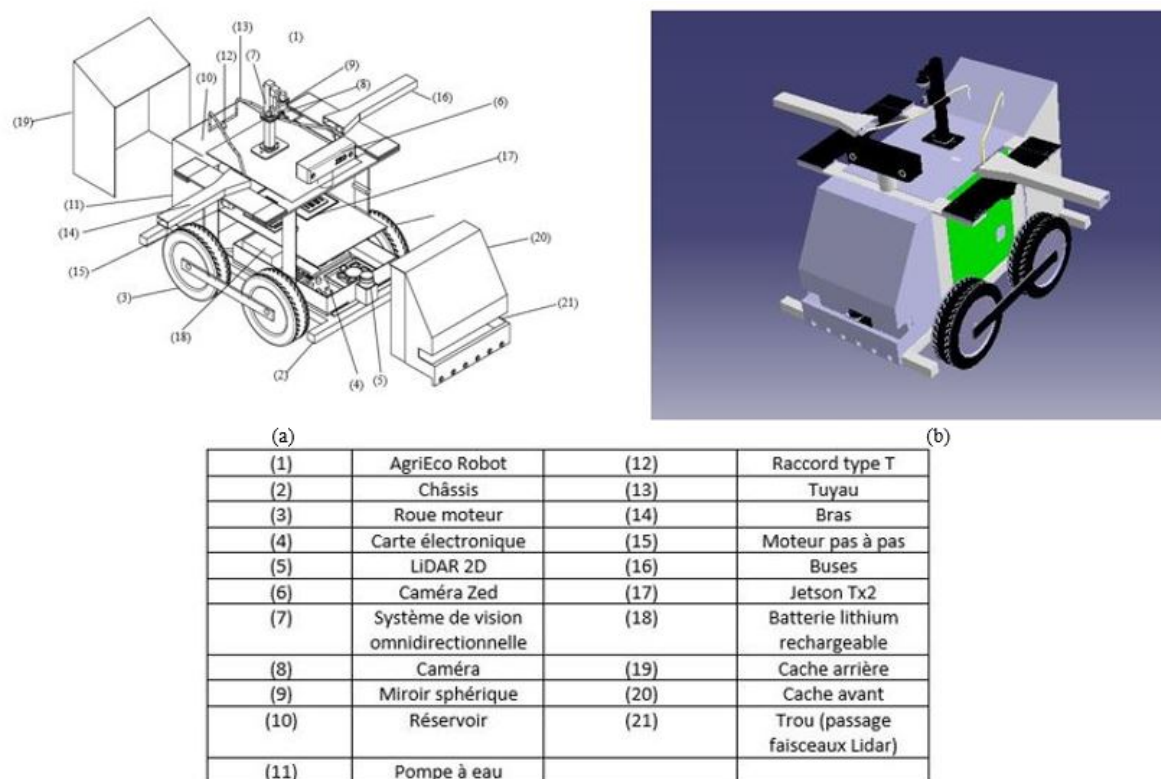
(a) La cartouche d'AgriEco Robot, (b) Conception CAD 3D Vue isométrique de la plateforme mobile AgriEco Robot
